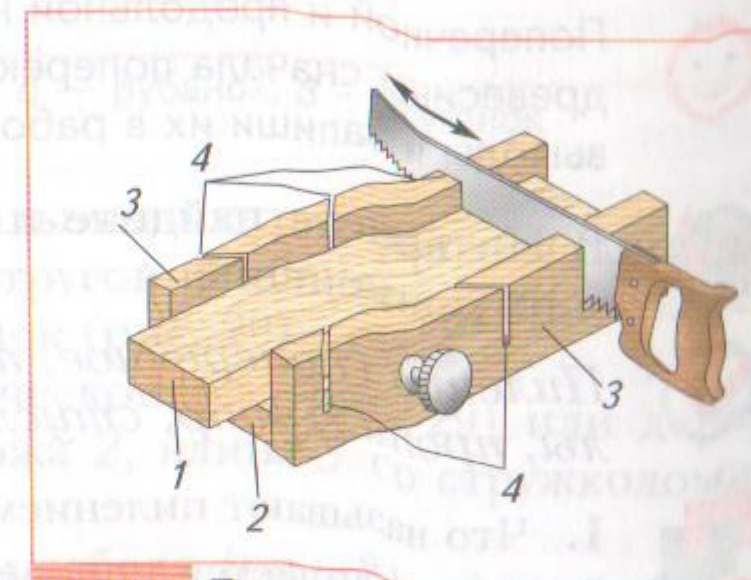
Пиление в стусле: 1 — заготовка; 2 — основание стусла; 3 — боковины; 4 — пазы
